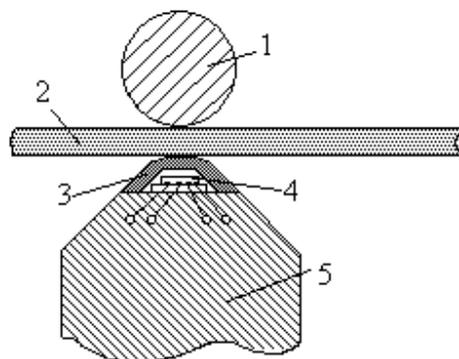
Разрез магнитного стенкомера: 1 – ферромагнитный шар; 2 – измеряемая стенка; 3 – защитный колпачок; 4 – датчик Холла; 5 – постоянный магнит
